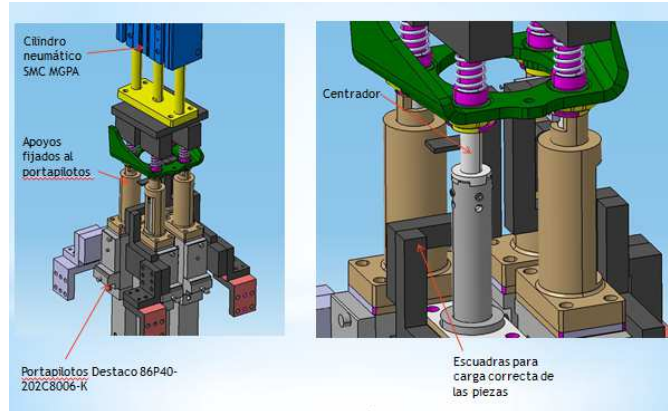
Ferramenta de soldadura em fase de anteprojecto
